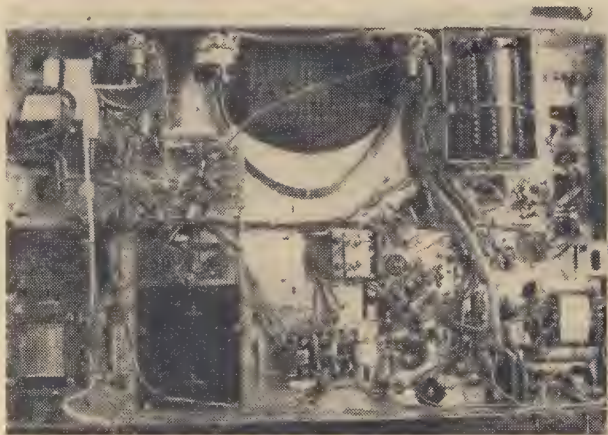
Unteransicht des Chassis, Blick in die Verdrahtung. Vgl. mit Bild 7
